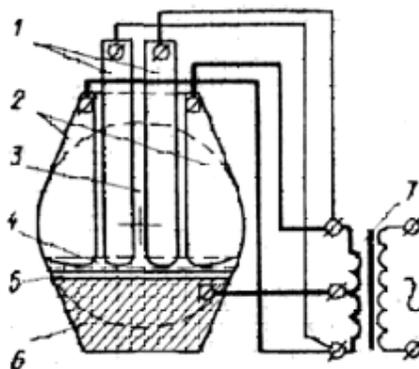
Схема ЭШС пластинчатыми электродами (ШП) заготовок переменного сечения: 1 — пластинчатые электроды подвижные, имеющие прямоугольную форму; 2—пластинчатые электроды неподвижные, имеющие форму заготовки; 3 — свариваемая заготовка; 4 — шлаковая ванна; 5 — металлическая ванна; 6 — металл шва; 7 — сварочный трансформатор
